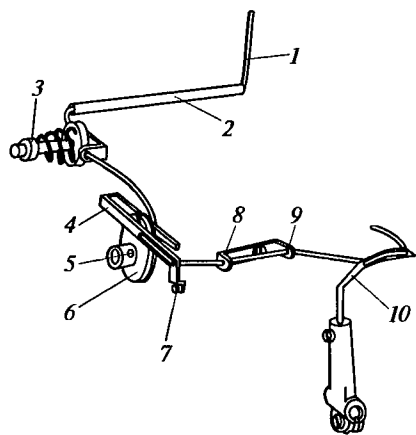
Схема трассы заправки нитки петлителя для образования двухниточного цепного стежка в стачивающе-обметочных машинах завода «Агат»
